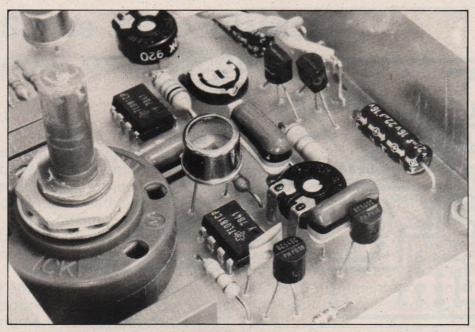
La photodiode est soudée en conservant toute la longueur des pattes
